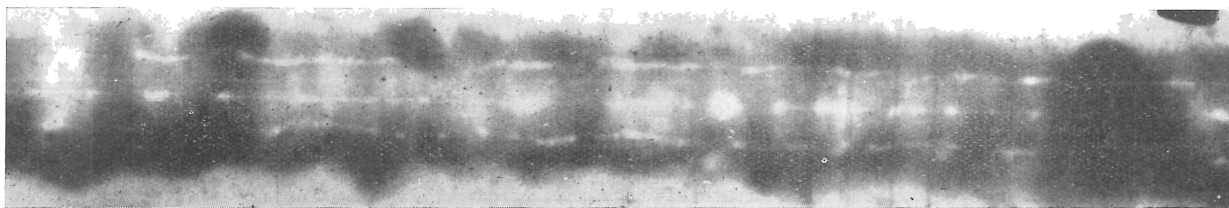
Radiographie d'une soudure en X (épaisseur 15 mm) : manque de pénétration et manque de liaison.
